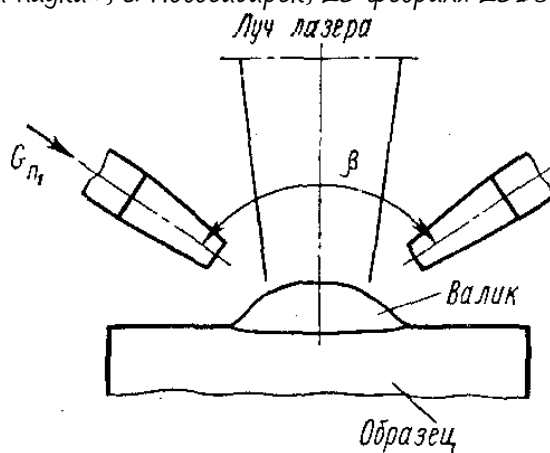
Схема двухсопловой подачи порошка при газопорошковой лазерной наплавке
